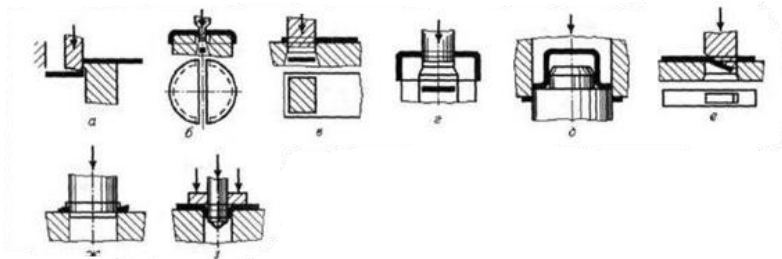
Типы разделительных операций листовой штамповки: а – отрезка; б – разрезка; в – вырубка; г – пробивка; д – обрезака; е – надрезка; ж – зачистка; з – проколка
